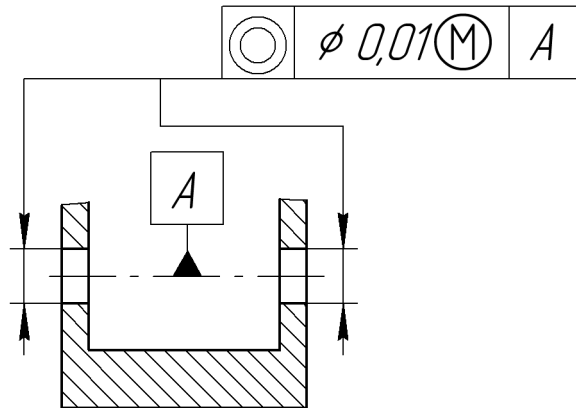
Простановка допуска расположения поверхностей
